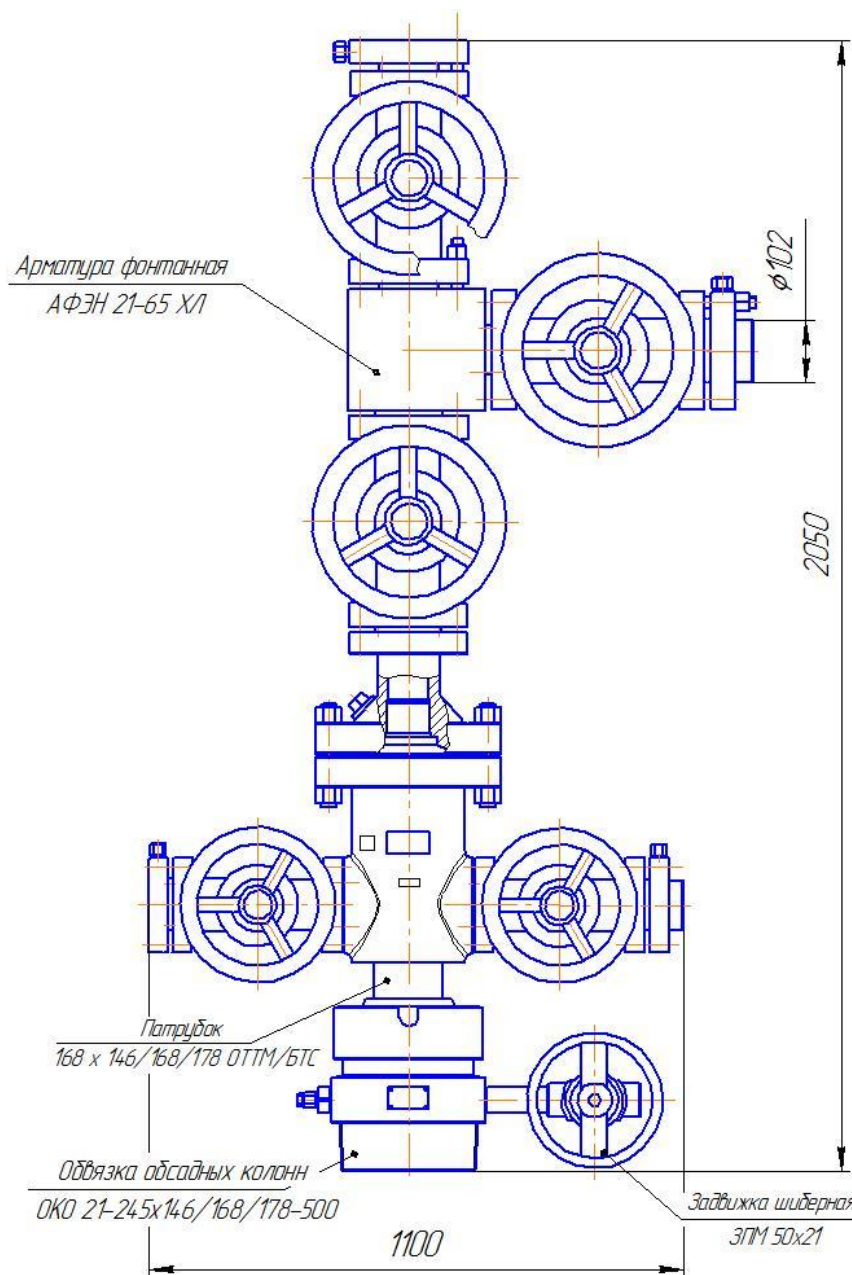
Схема монтажа фонтанной арматуры АФЭН 21-65 П на обвязке обсадных колонн ОКО 21-245x146/168/178-500.
